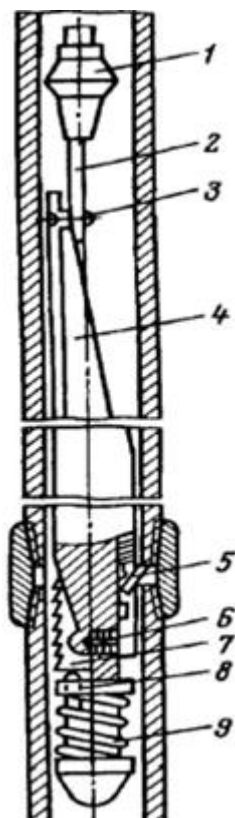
Схема отклонителя висячего типа, устанавливаемого на стыке труб: 1 – райбер; 2 – направление; 3 – болт; 4 – отклонитель; 5 – защелка; 6 – фиксатор; 7 – плашка; 8 – шток; 9 – пружина
